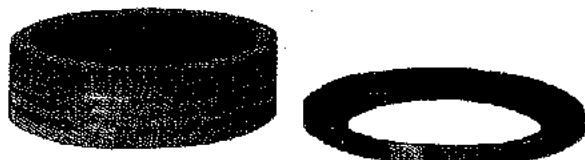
Muela cilíndrica y aro de adaptación (Blanchard Machine Co.)
